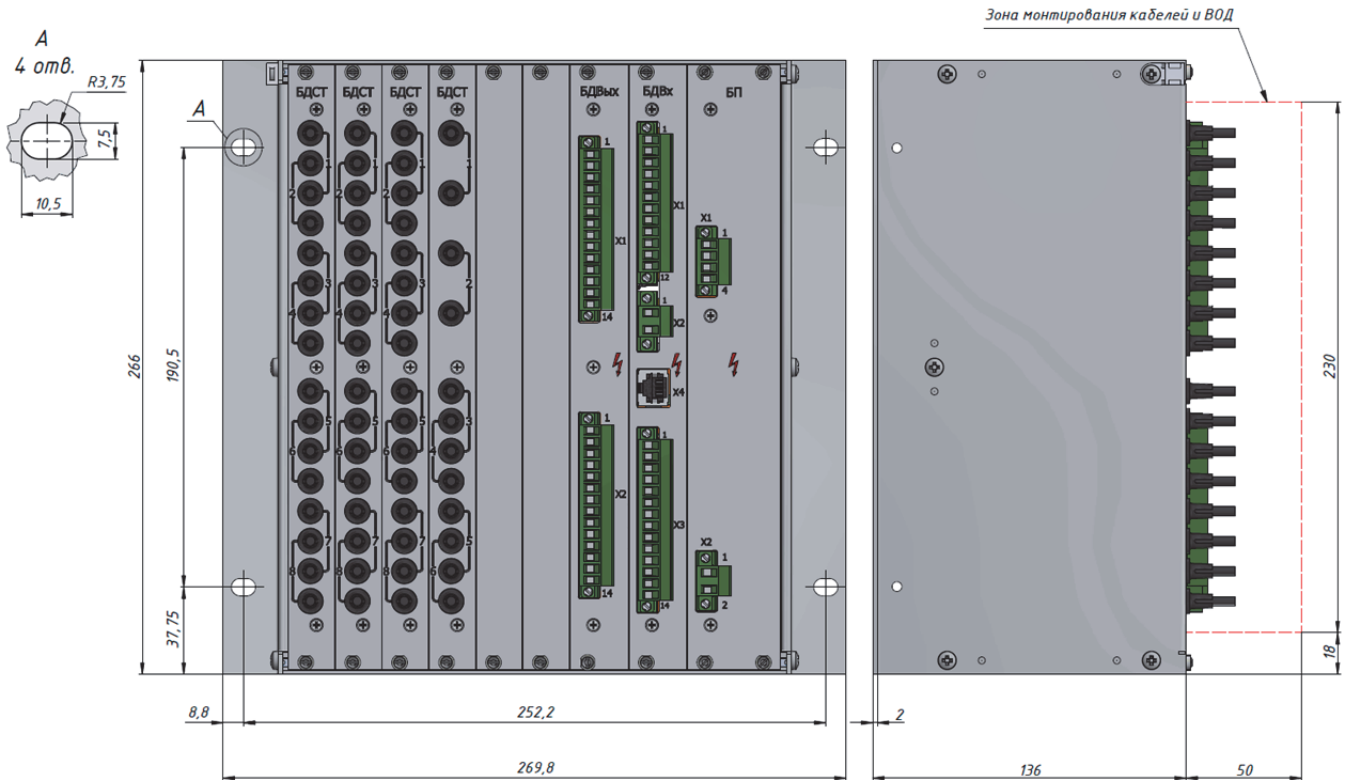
Внешний вид и габаритные размеры БПМ (исп.01).
